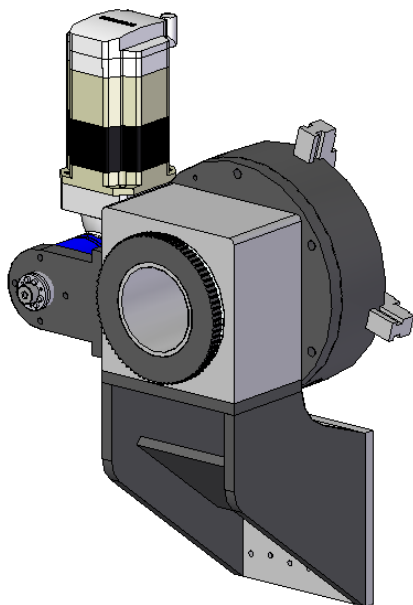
Estrutura de chapa soldada para o suporte bucha.
